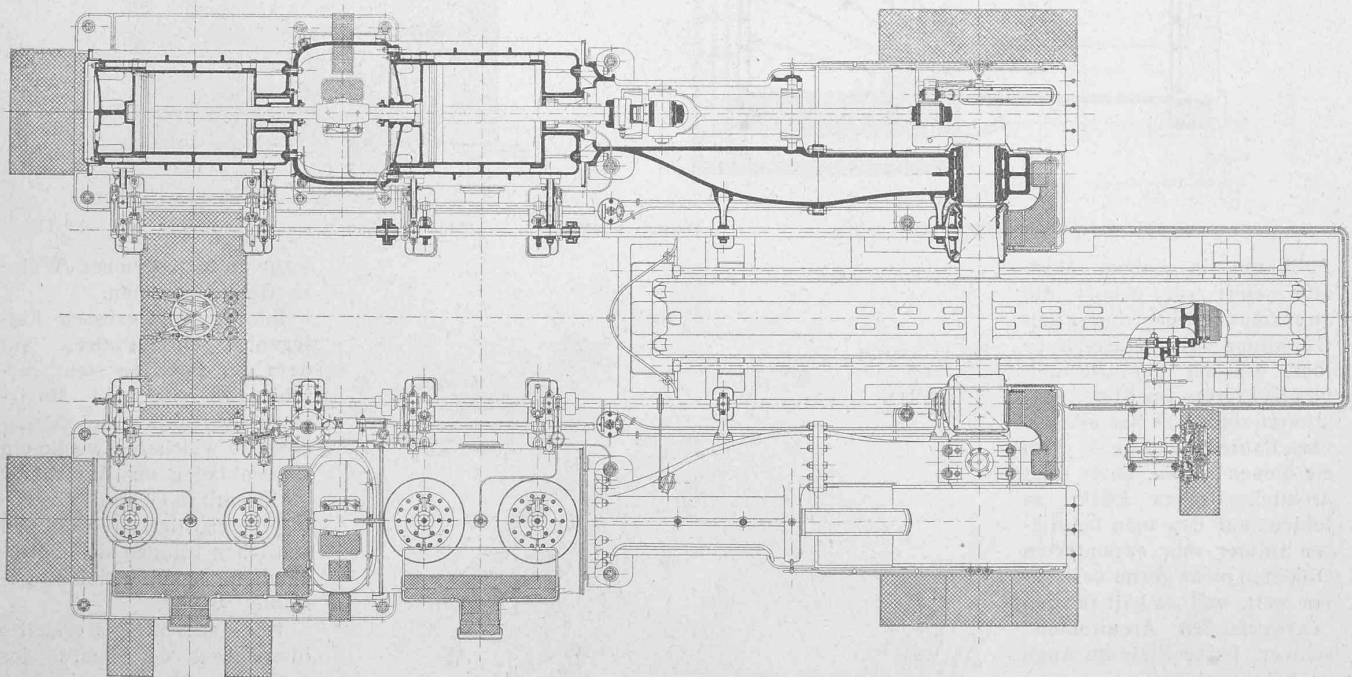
Grundriss. — Schnitt durch die Mitteldruckseite und Ansicht der Hochdruckseite.
